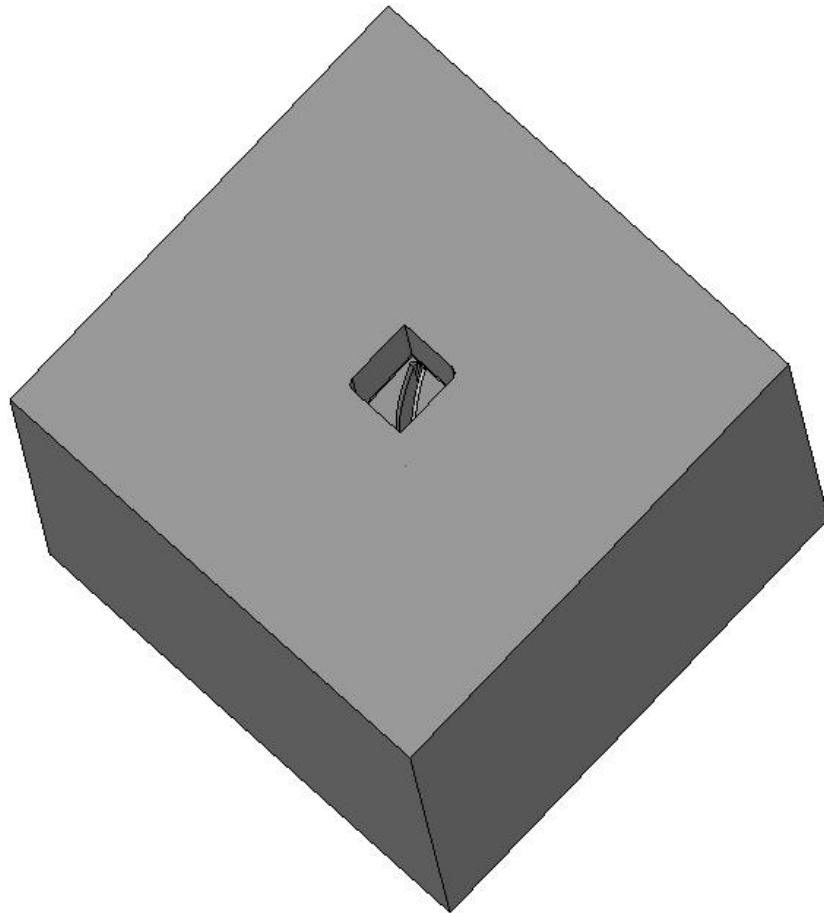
3D модель матриці штампу для видавлювання заготовок компресорних лопаток
